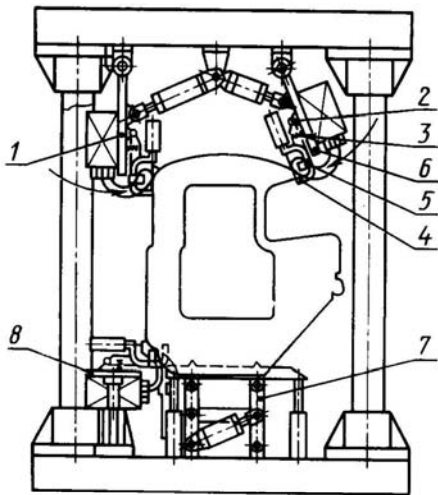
Схема сварки кабины на много-электродной машине
